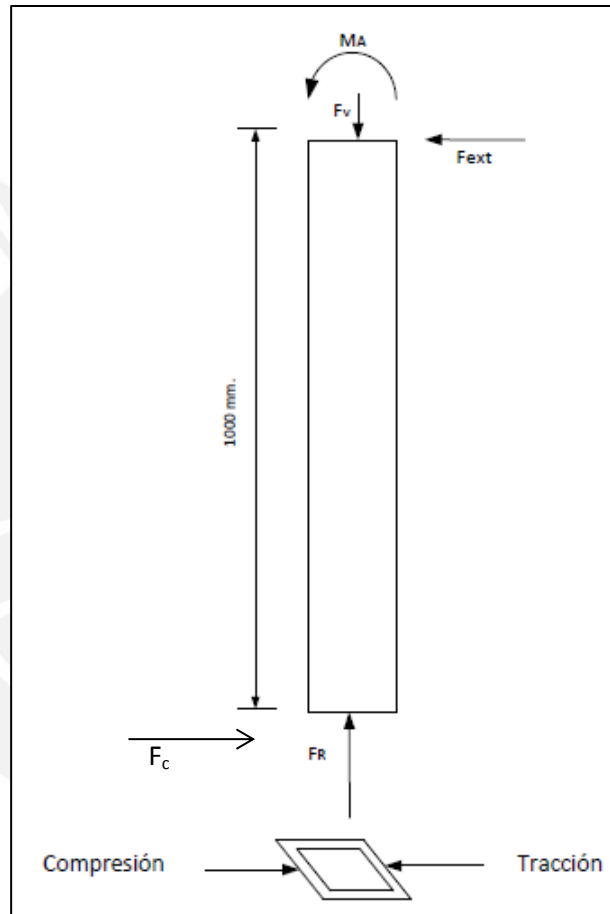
DCL de fuerzas y momentos en el cordón de soldadura
